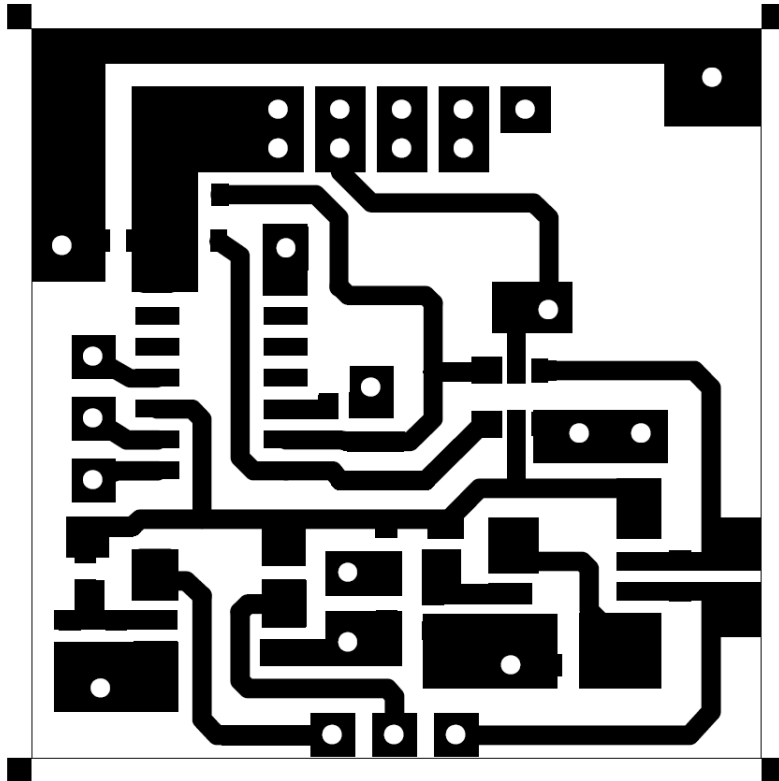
Disseny de la capa superior de la PCB que conté l'ATtiny.
